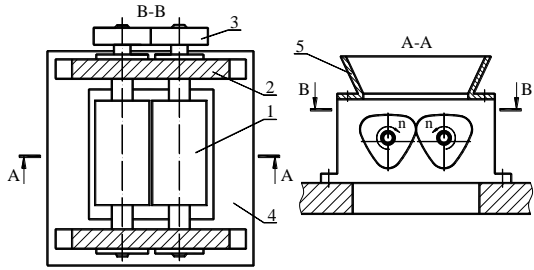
Роторний ножовий подрібнювач: 1 – ротор; 2 – ніж ротора; 3 – ножі статора; 4 – корпус; 5 – решітка
